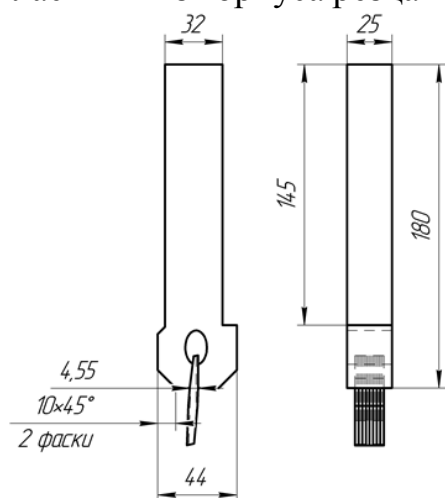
Сборный долбежный резец с установленной пластиной
